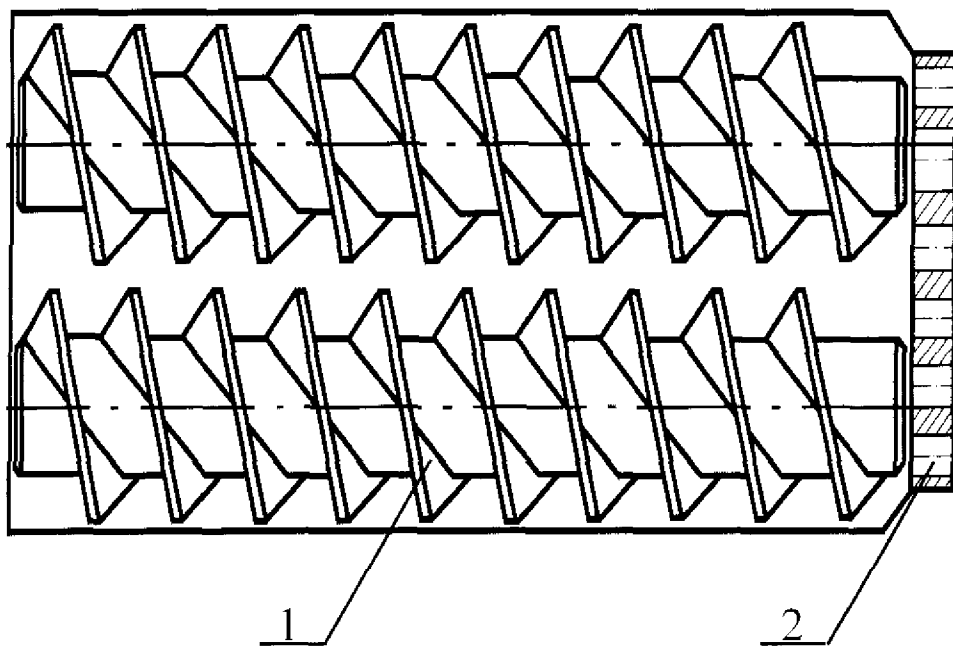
Прес–гранулятор: 1- пресувальний вал, 2- перфорована решітка
